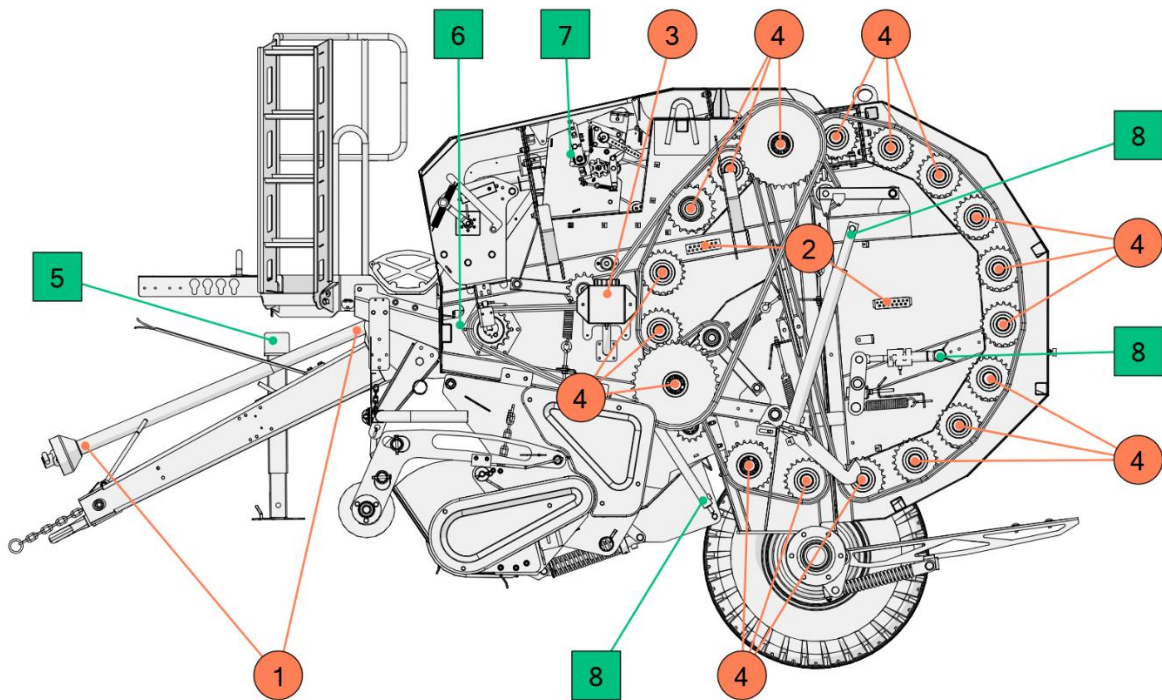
Маркировка основных точек смазки пресс-подборщика
